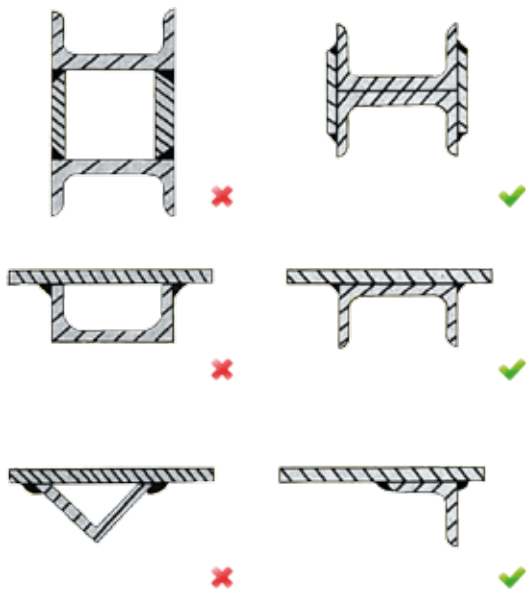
Lasverbindingen_Assemblages soudés
